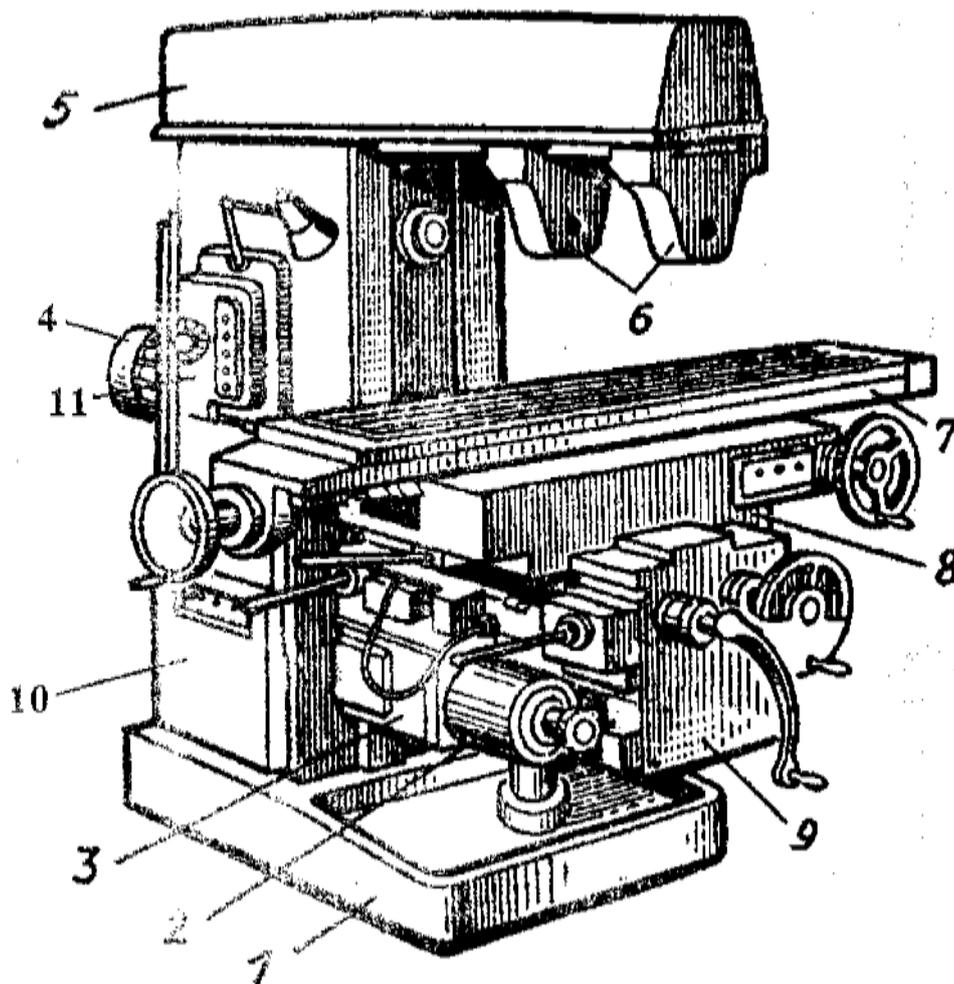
Универсальный консольный горизонтально-фрезерный станок мод. 6Р82Ш
